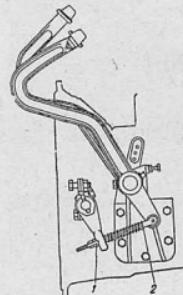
Привод механизма сцепления автомобиля ЗИС-5
